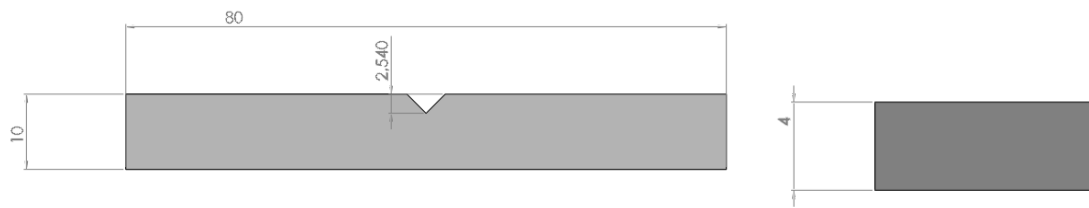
Dimensões do provete de impacto, espessura do provete de impacto
